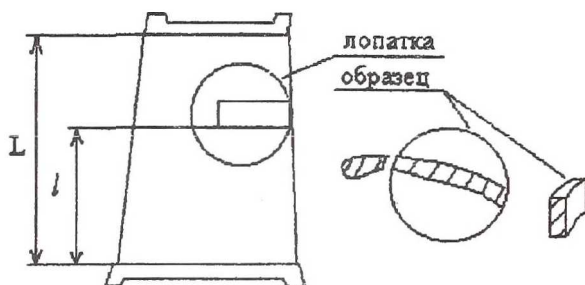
Схема подготовки образца из лопатки турбины ($l = 2/3 L$)
